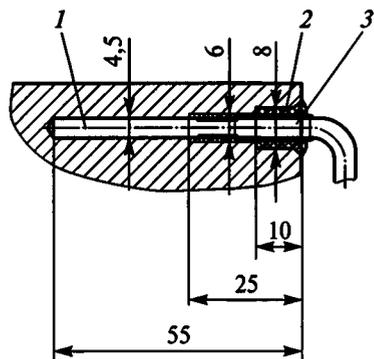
Установка датчика температурного контроля подшипника в подшипниковый щит: 1 — терморезистор; 2 — резиновая предохранительная трубка; 3 — провода терморезистора
